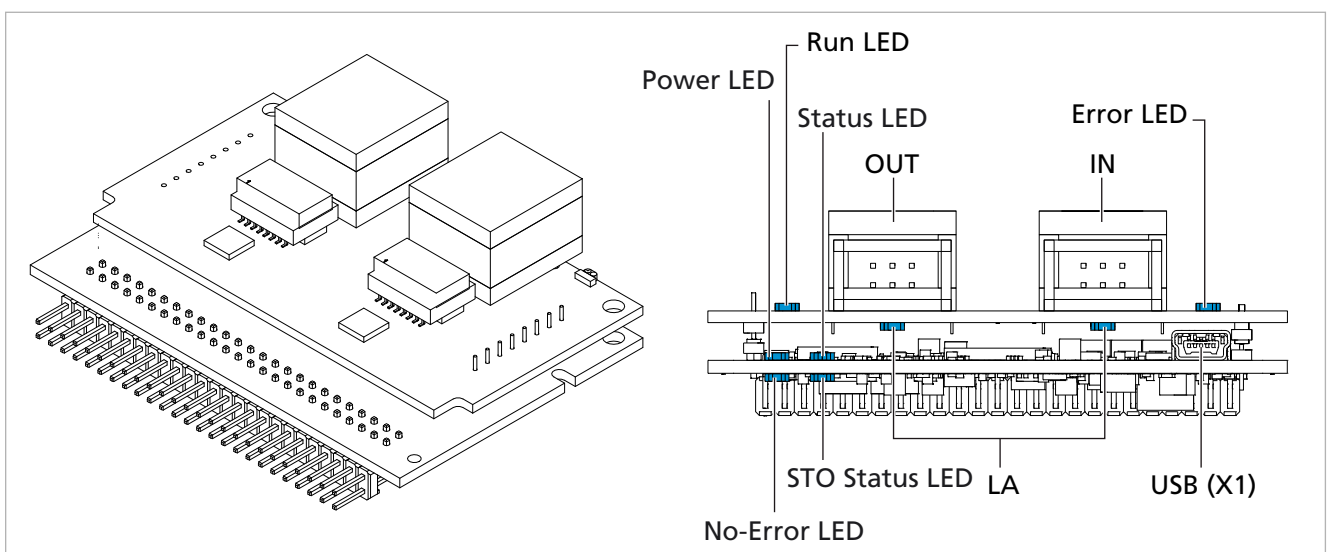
Isoansicht (links) und Frontansicht (rechts) der aufgesteckten EtherCAT-Platine
